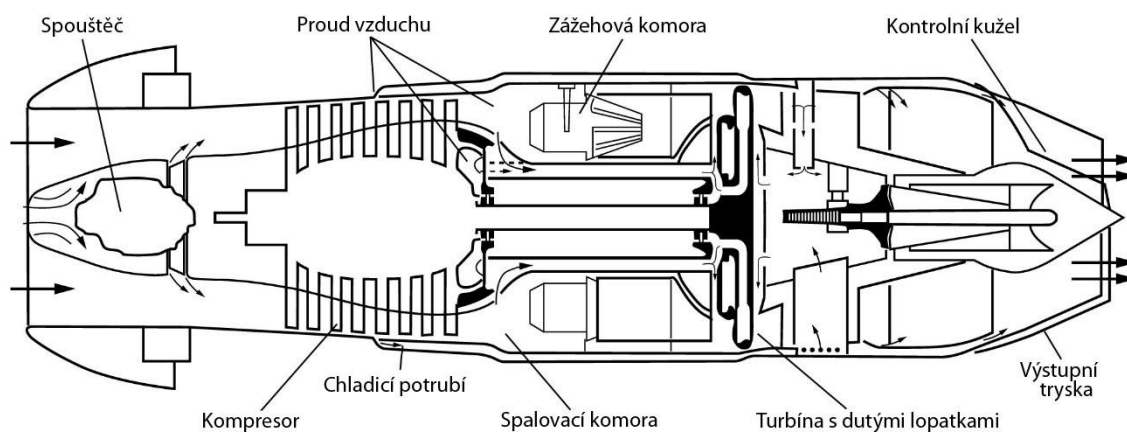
Princip prvního proudového motoru [8, upraveno]
